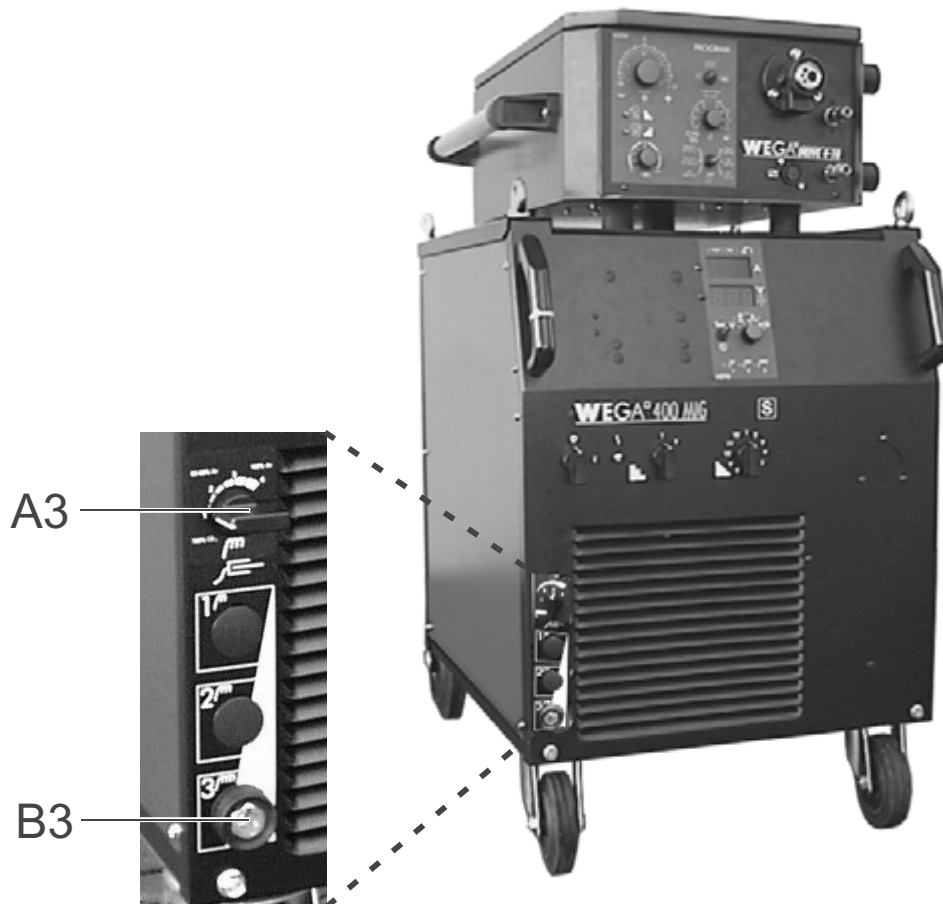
/5; Frontansicht (WEGA 400 MIG E mit elektronischer Drossel)
